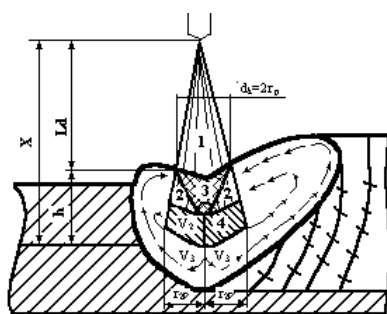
Принципиальная схема движения расплава в сварочной ванне
